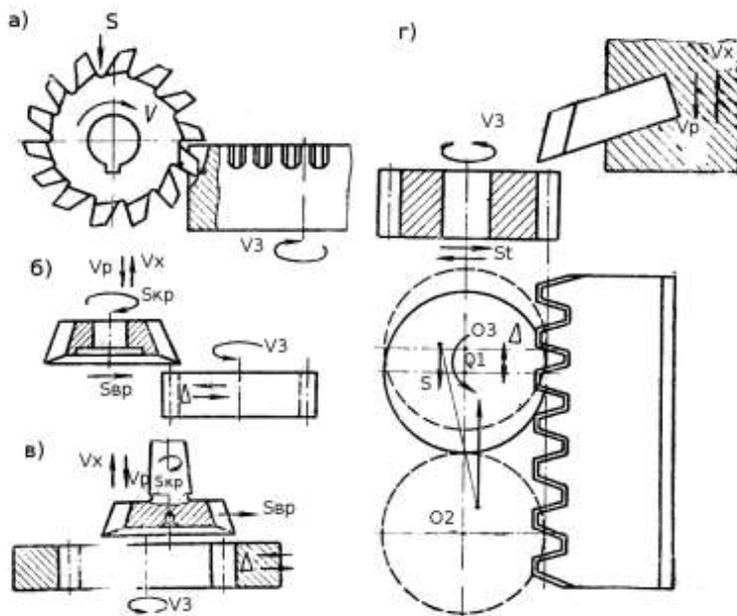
Нарезание зубчатых колес: а — червячной модульной фрезой; б, в — зуборезным долбяком; г — зуборезной гребенкой.
